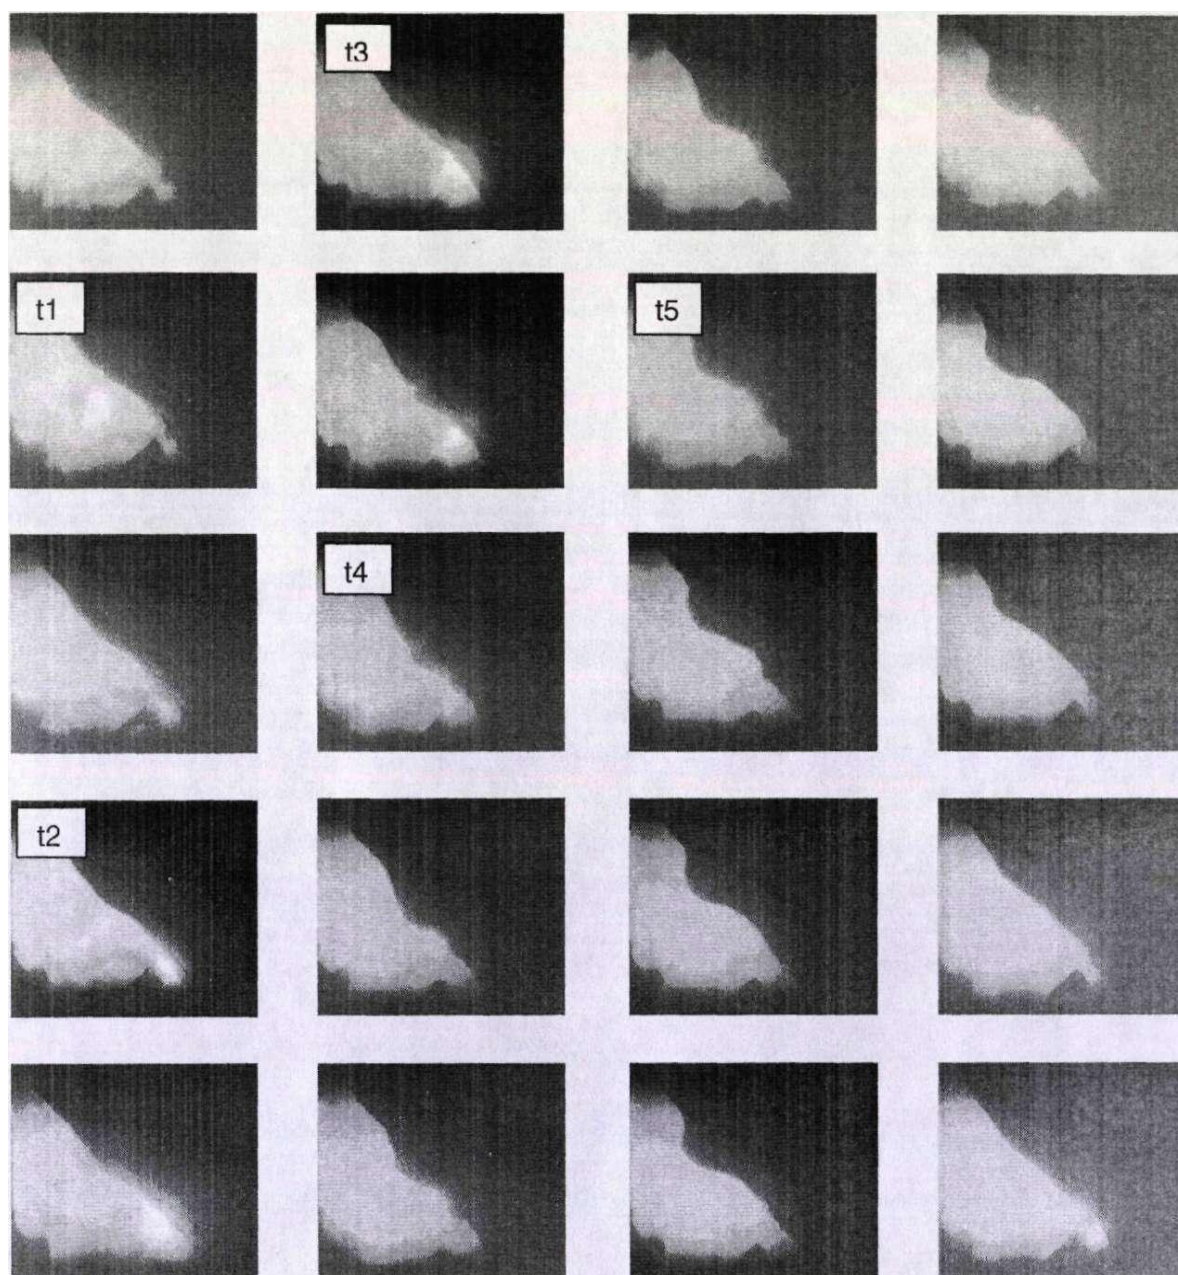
Движение металла по сварочной ванне в полупотолочном положении.
